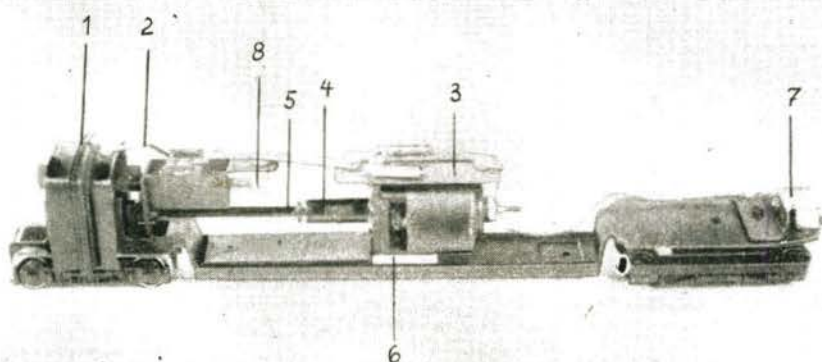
Das Triebwerk; 1 = Befestigungsschraube des Faltenbalgs, 2 = Kontaktfeder 28-14, 3 = Entstörplatte 11-14, 4 = Mitnehmer, 5 = Kardanwelle 30-14 / 63 mm, 6 = Lager 10-14, 7 = Beleuchtungseinrichtung (gehört zum Fahrwerk), 8 = Glühlampe für Innenbeleuchtung 16 V, Stecksockel 5 mm
